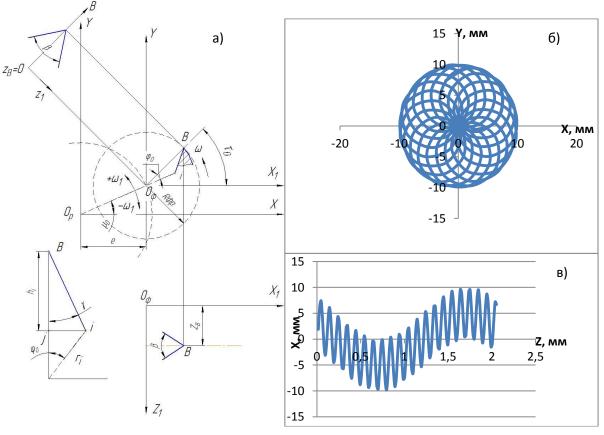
Анализ траектории движения зуба резьбовой фрезы: а - расчетная схема; б - траектория движения инструмента в системе координат XY; в - траектория движения инструмента в системе координат XZ.
